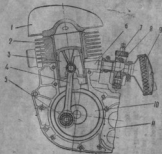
Блок двигателя с коробкой передач в разрезе.
